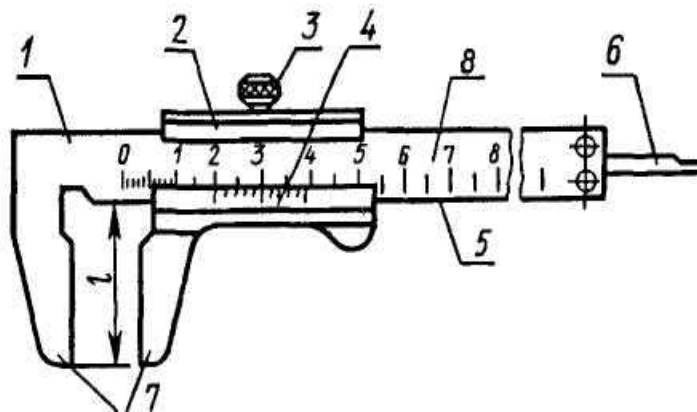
1 – штанга; 2 – рамка; 3 – затискувач; 4 – ноніус; 5 – робоча поверхня штанги; 6 – глибиномір; 7 – губки з плоскими вимірювальними поверхнями для вимірювання зовнішніх розмірів; 8 – шкала штанги
